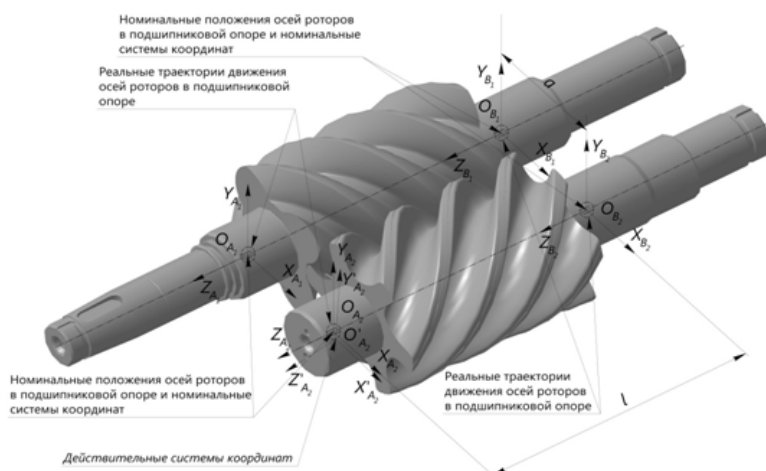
Расчетная схема положения роторов в подшипниковой опоре
